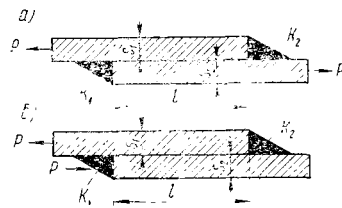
Работа сварных соединений внахлестку с двумя лобовыми швами:
